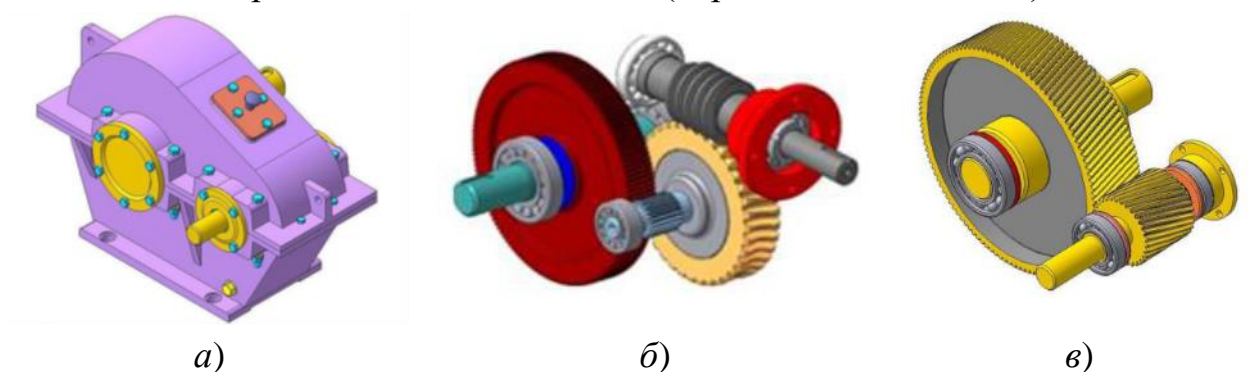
а) - Цилиндрический зубчатый одноступенчатый редуктор; передачи зацеплением: б) цилиндрическая зубчатая и червячная, в) - цилиндрическая зубчатая
